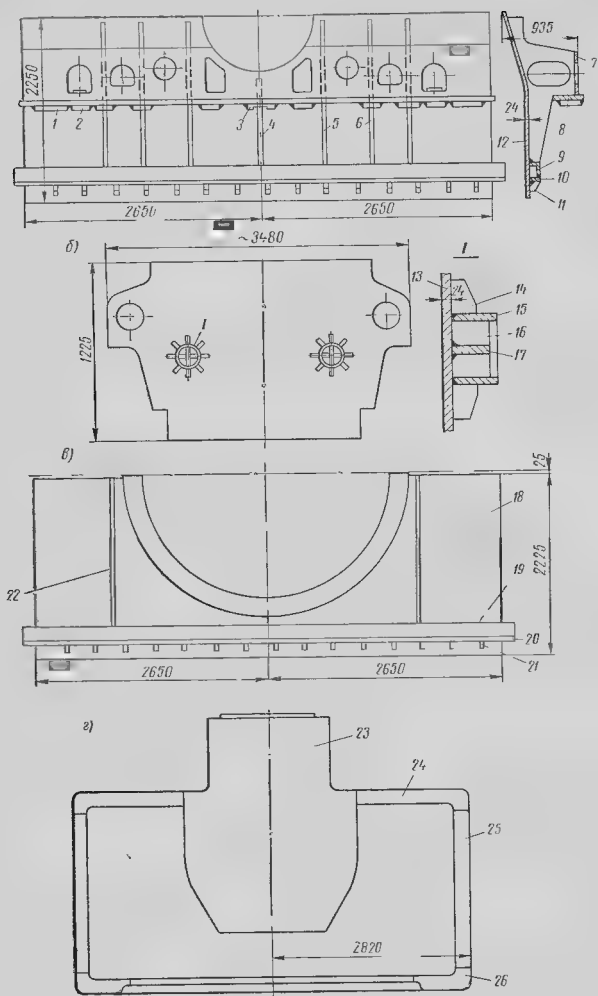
Сборка и сварка отдельных узлов выходной части цилиндра низкого давления: а — задняя стенка; б — боковая стенка; в — передняя стенка; г — горизонтальный фланец с корпусом подшипника
